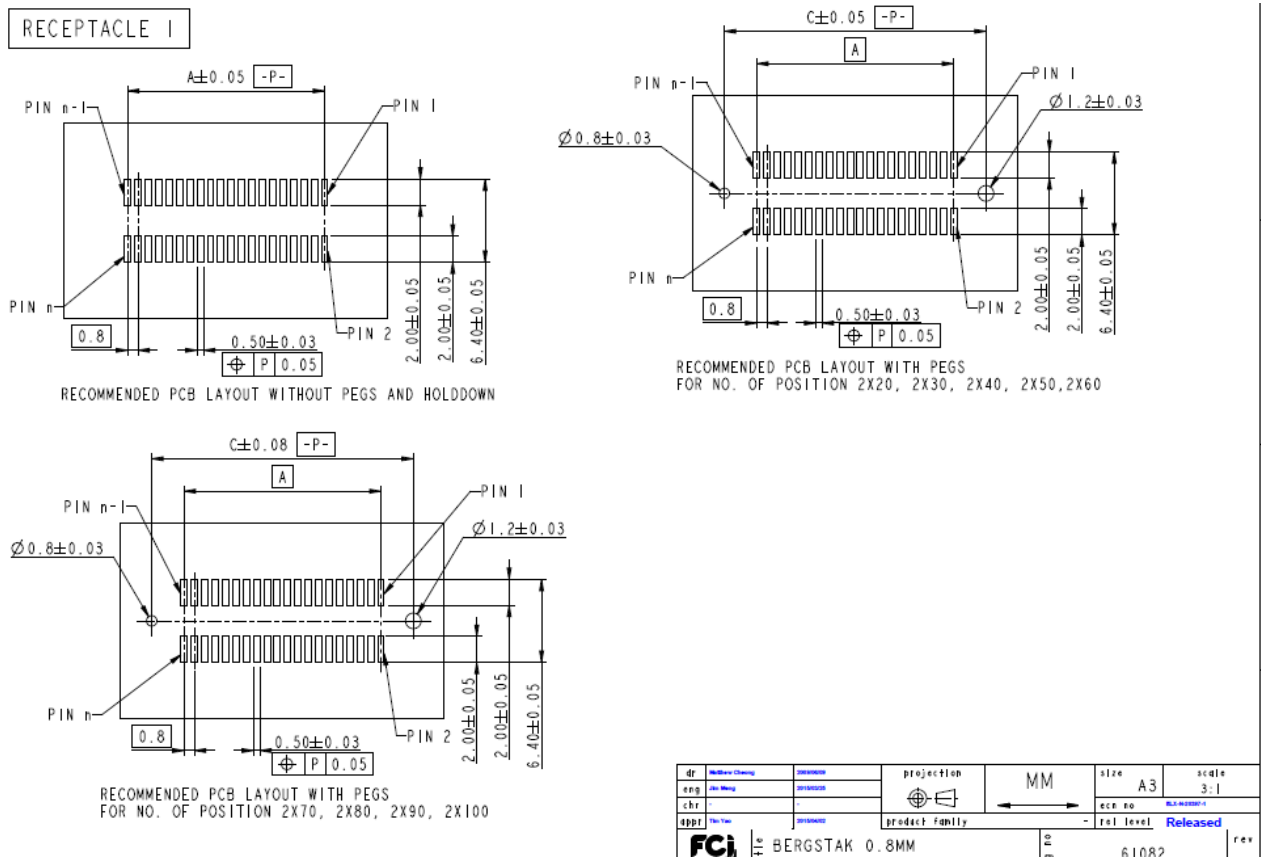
间距 0.8mm 立式双排 80 PIN PCB 封装
